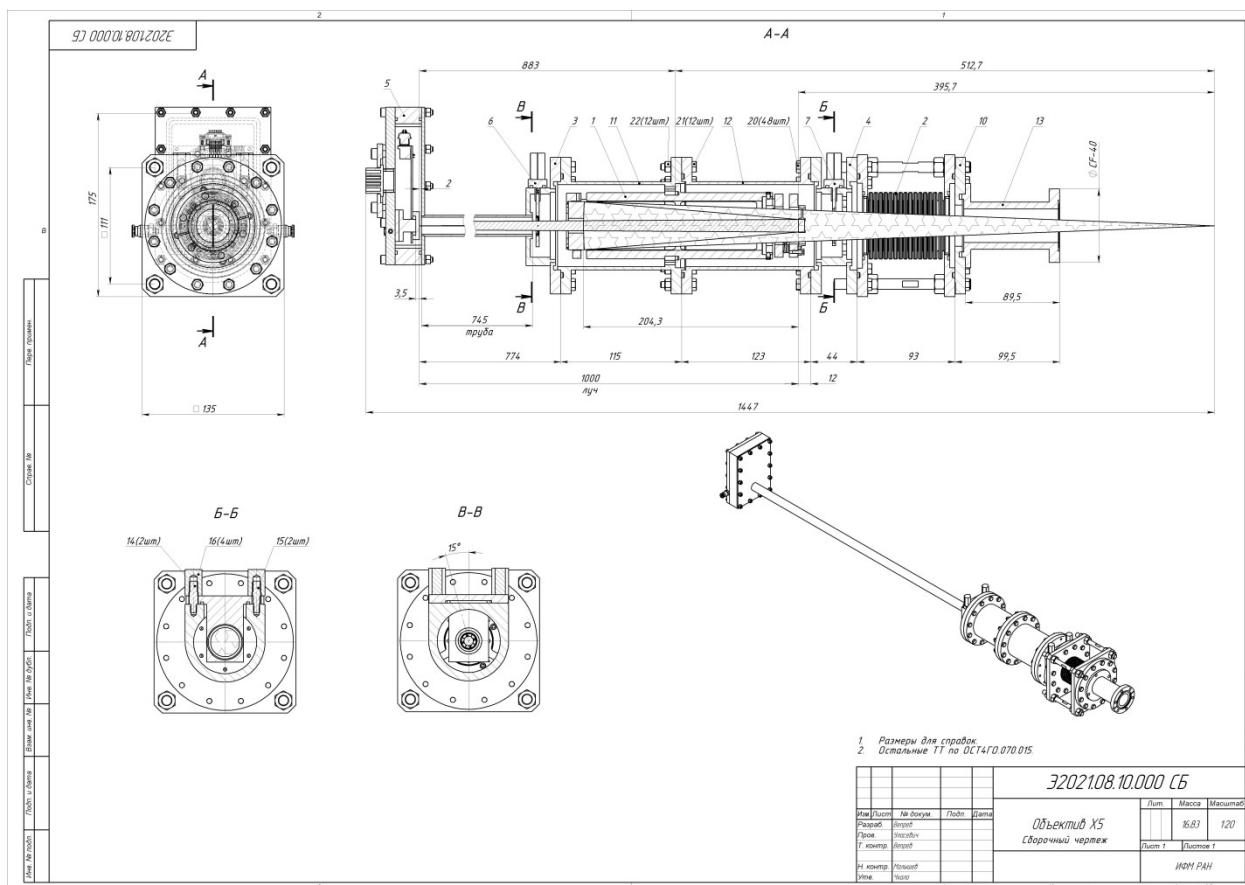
Сборочный чертёж микроскопа для имиджинга лазерного факела
